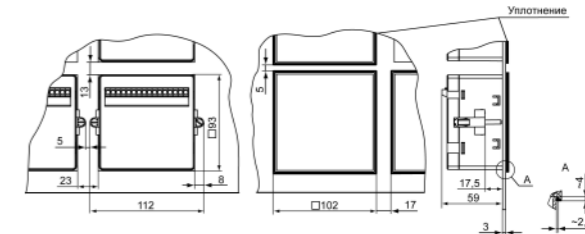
Прибор в корпусе Щ1, установленный в щит толщиной 3 мм
